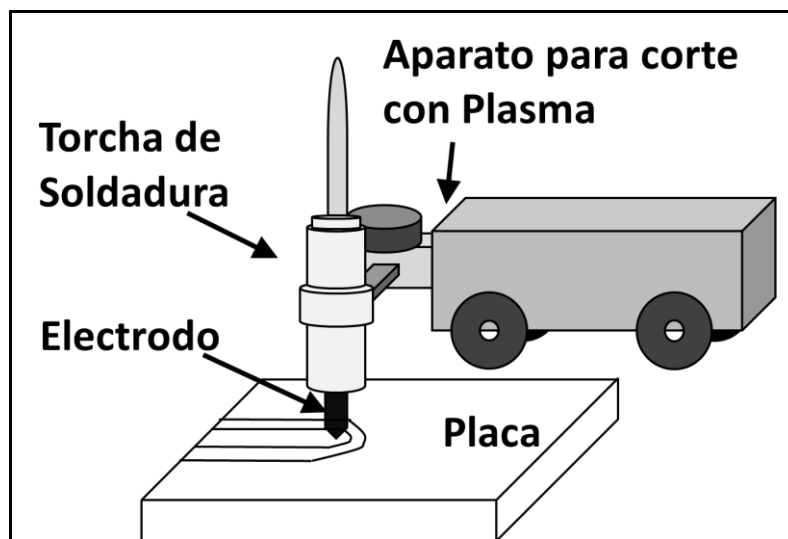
Esquema de la adaptación de la antorcha de soldadura GTAW a la máquina de corte con plasma.
